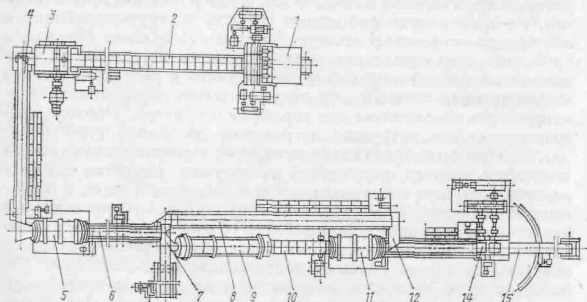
Агрегат для дробления и сортировки крупногабаритного легковесного лома
